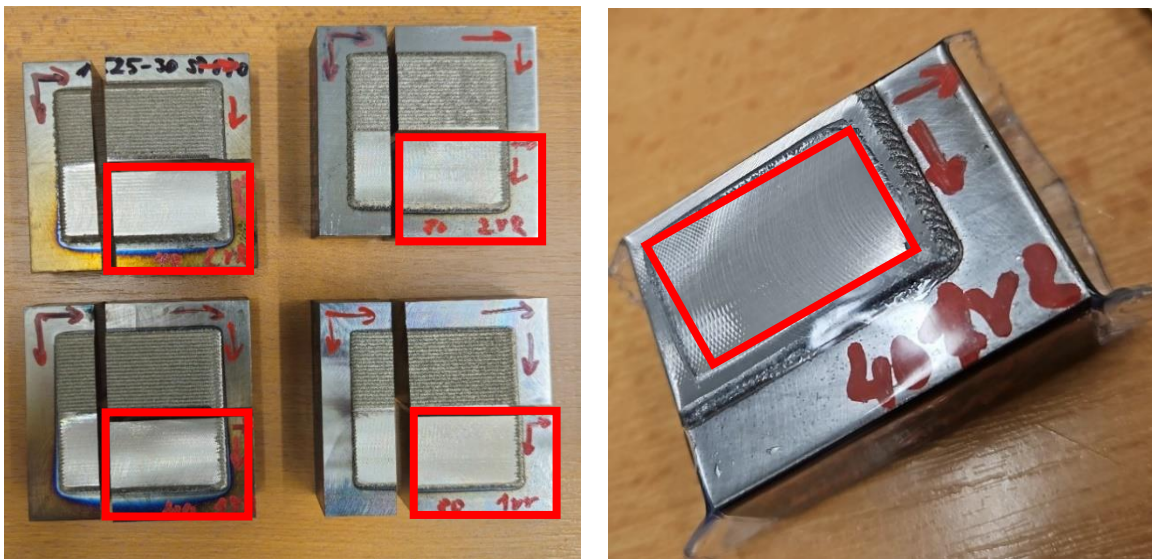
Princip částečného obrobění návaru – spodní vyznačená část frézována, návar Stellite 21, 80 cm/min, 2 vrstvy
